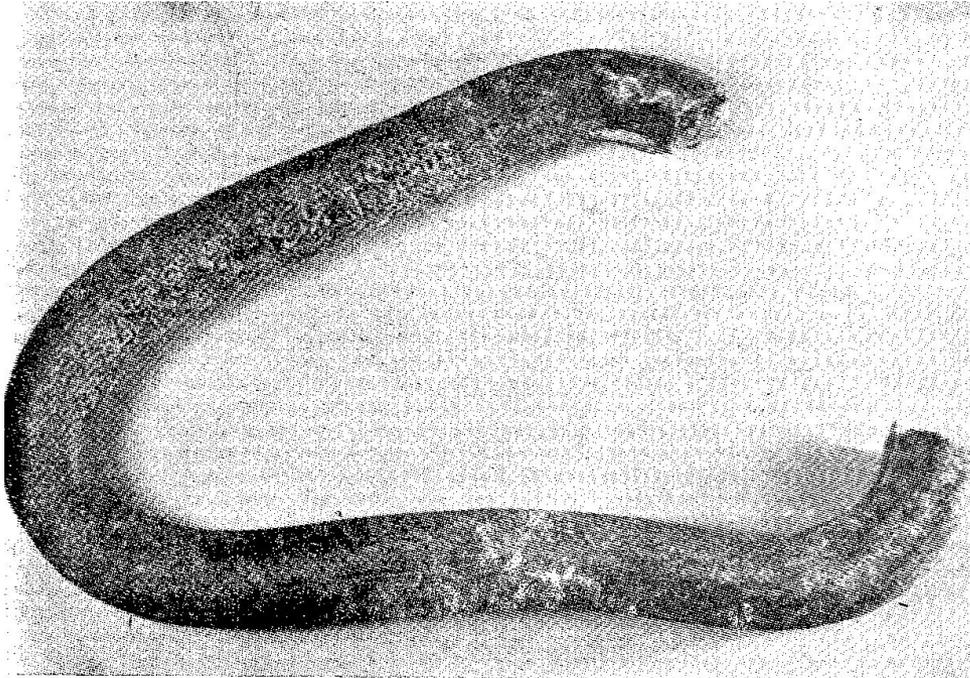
Разрушенное из-за плохого качества сварного соединения звена цепи:
